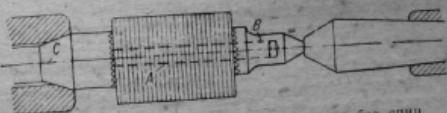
Оправка для фрезеровки колес с набором в промежутки между спицами.
